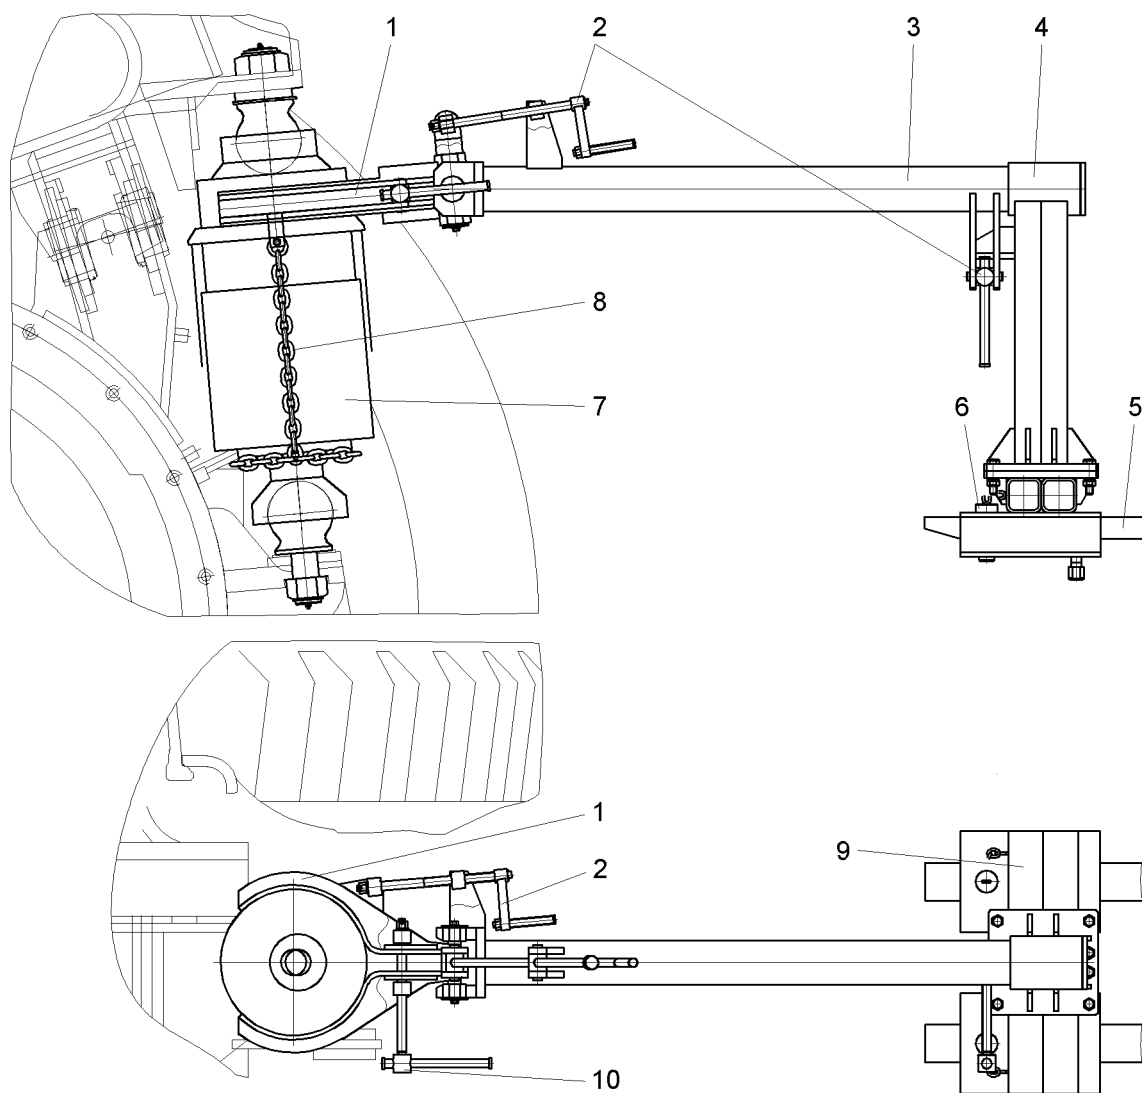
Приспособление для снятия и установки цилиндров подвески:
